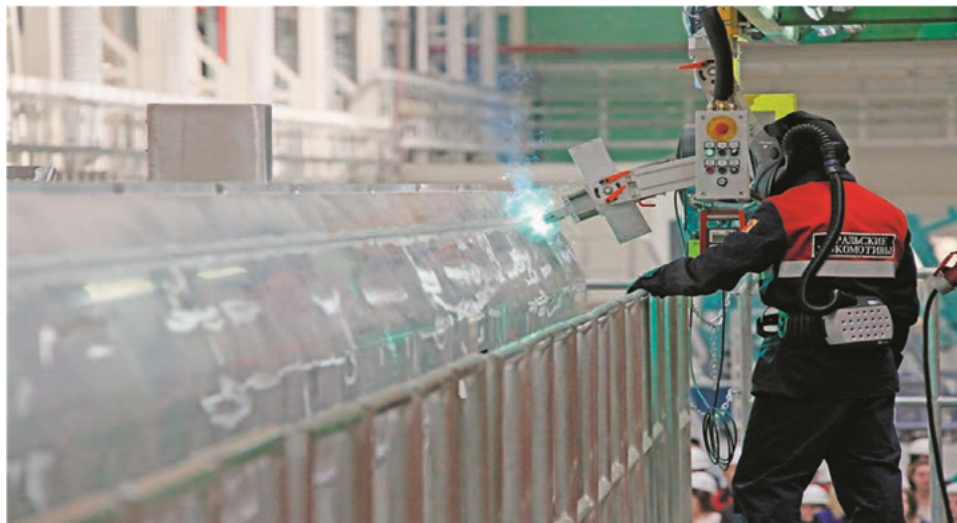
Роботизированная сварка алюминиевого корпуса в среде защитного газа на предприятии «Уральские локомотивы» [8]
